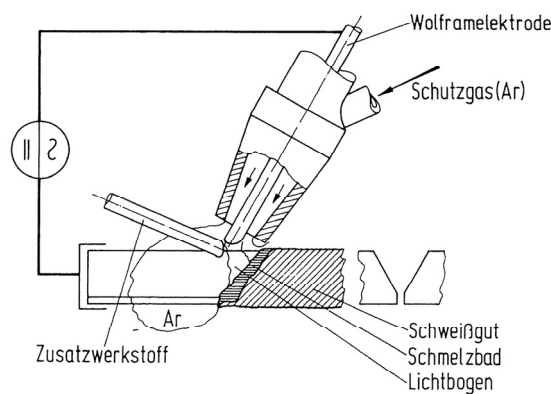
Wolfram-Inertgasschweißen [9]
